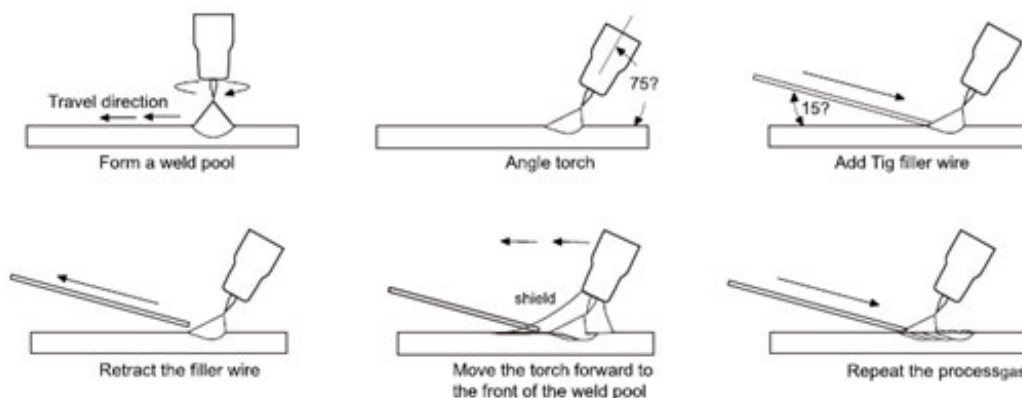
TIG-Schweißen mit Zusatzwerkstoff
